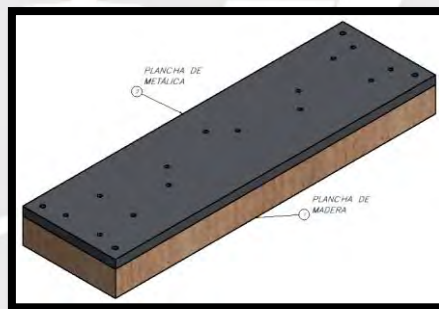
Plancha base de madera - Plancha base metálica.
